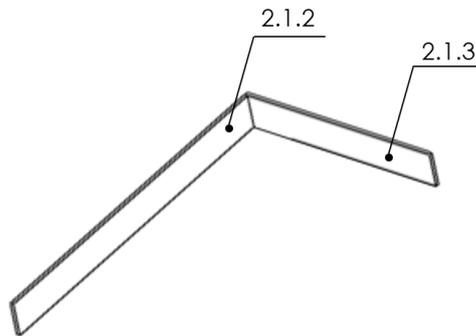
Ensamblaje subconjunto 2.1 mesa de centro. Soldadura 2
